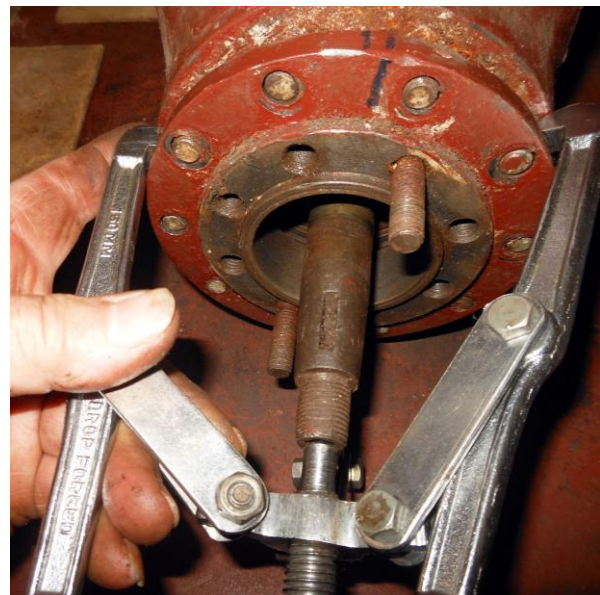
Установка винтового съемника для демонтажа корпуса шарикоподшипника
